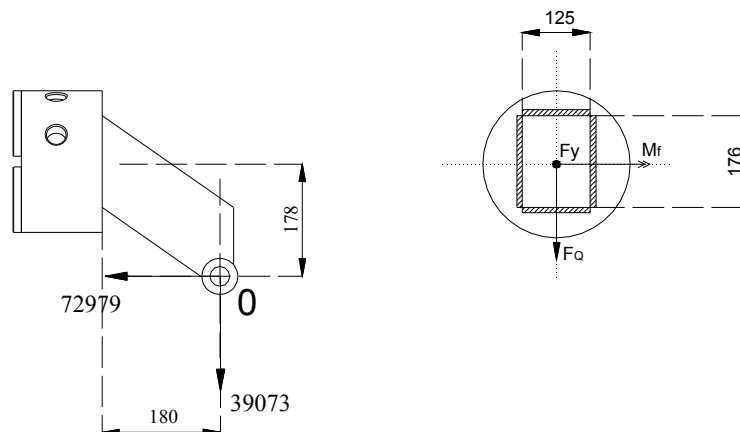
SOLDADURA EN LA BASE DEL PIVOTE
